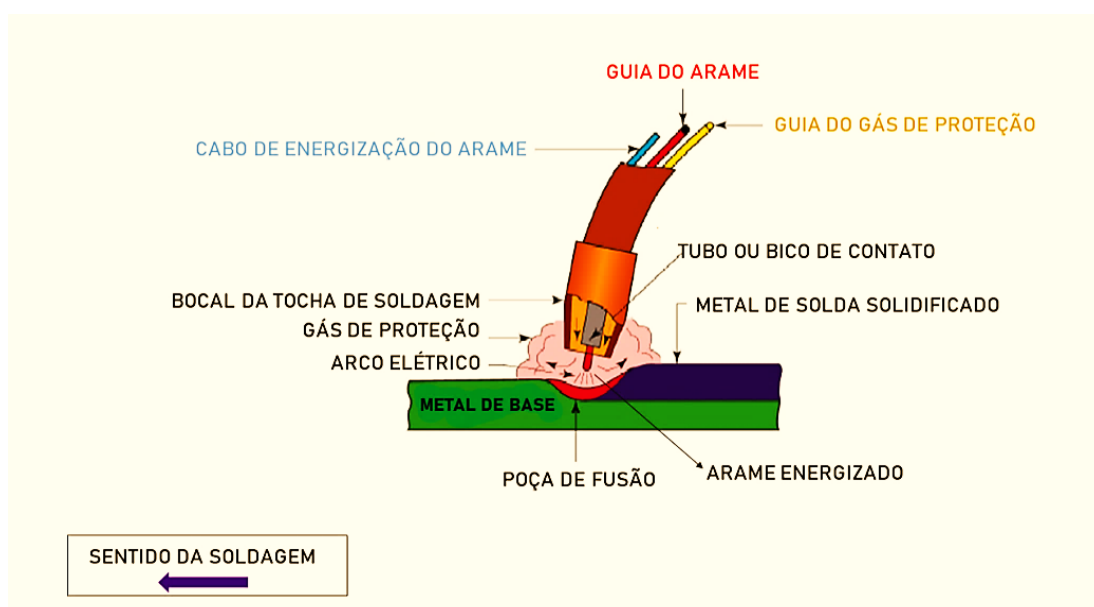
Esquema básico do processo de soldagem MIG/MAG
